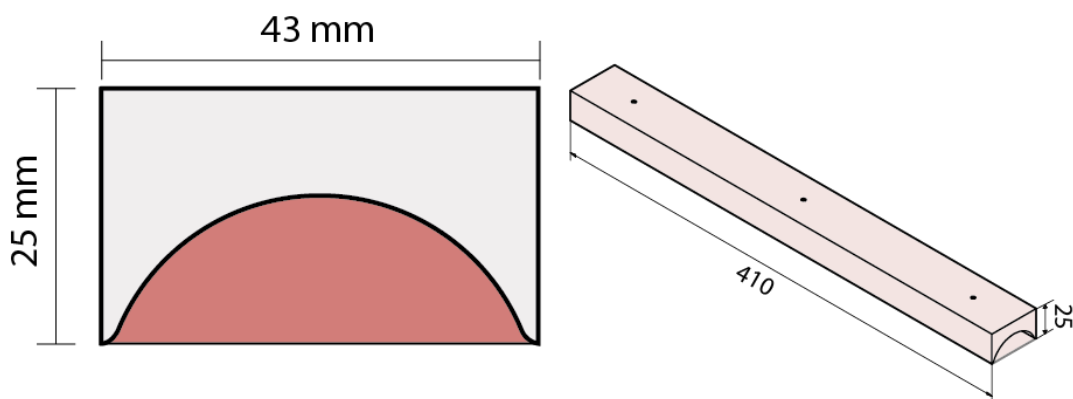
Dimensiones y desbaste del cuerpo cóncavo generador de bolas para corte en plancha de grilon
